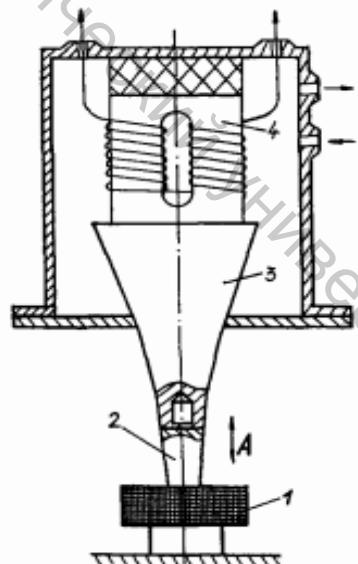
Схема установки для ультразвуковой сварки
